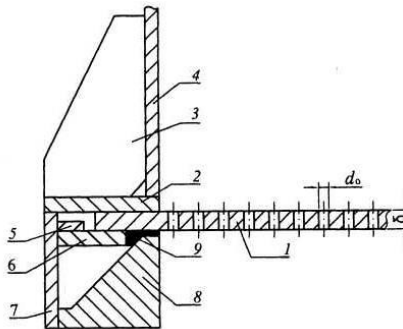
Крепление газораспределительной решетки: 1 – решетка; 2 – фланец; 3 – косынка; 4 – верхний корпус сушилки; 5 – ограничитель; 6 – опора; 7 – нижний корпус сушилки; 8 – фугеровка; 9 – уплотнительная набивка (асбестовый шнур)
